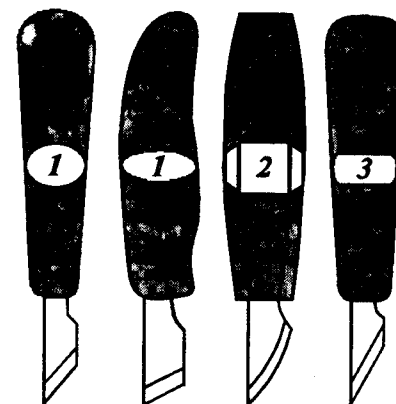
Виды ножей для резьбы по дереву с ручками различной формы: 1 – округлой; 2 – граненой; 3 – плоской
